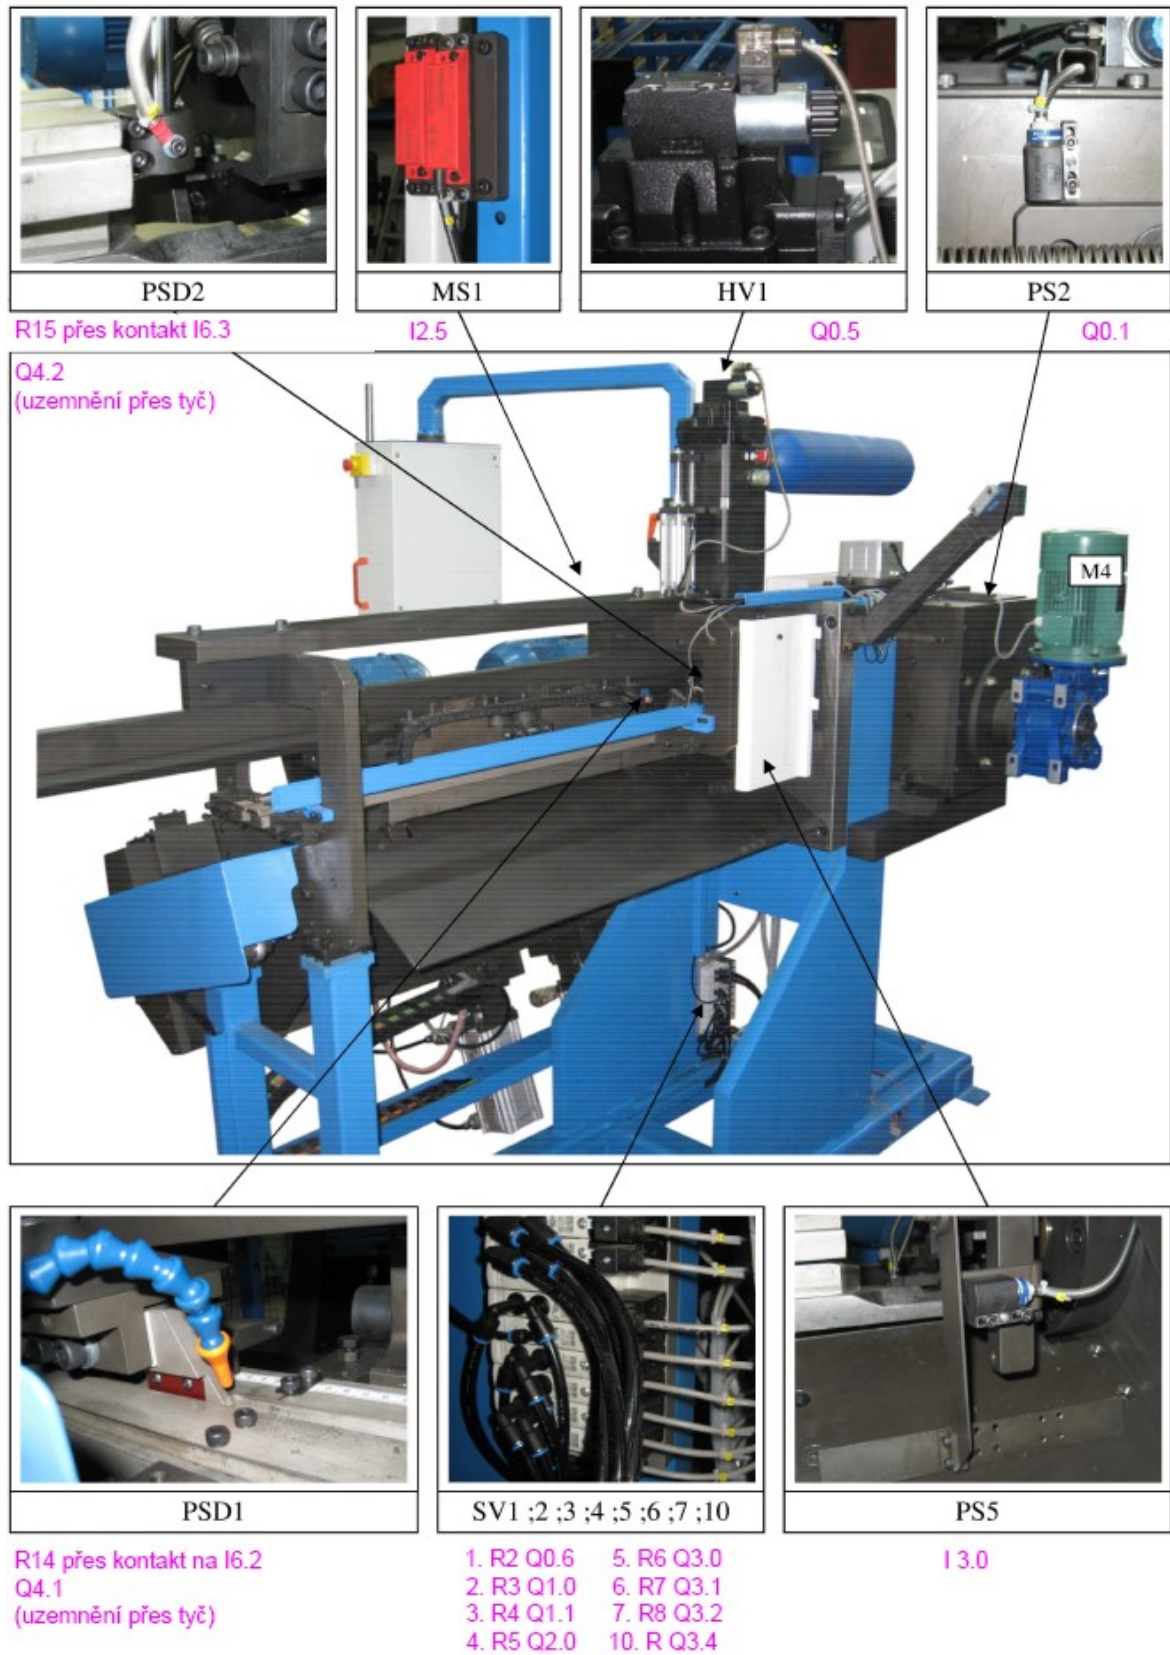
Dělicí centrum – Půdorys – Layout umístění prvků automatizace
